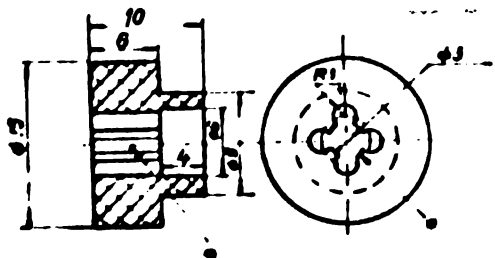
Piesă duză din ceramică prelucrabilă prin ultrasunete.
